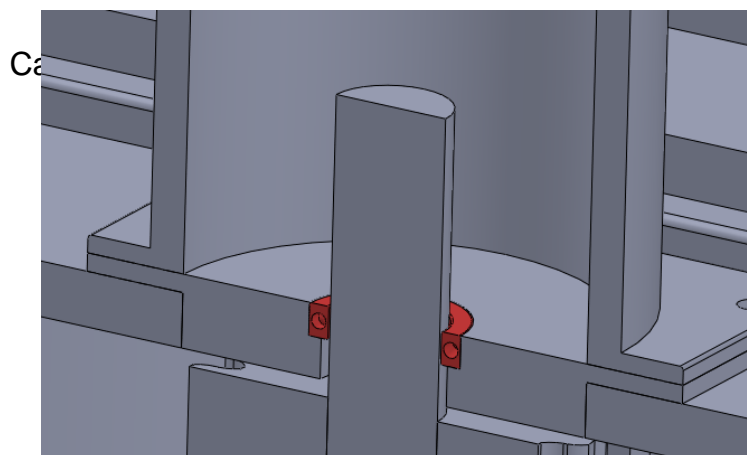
Posición del rodamiento superior (Marcado en rojo).
